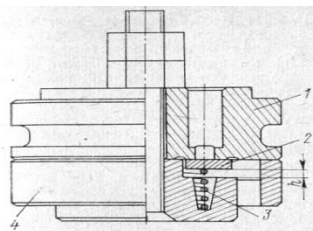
Клапан всасывающий кольцевой пластинчатый четвертой ступени.
